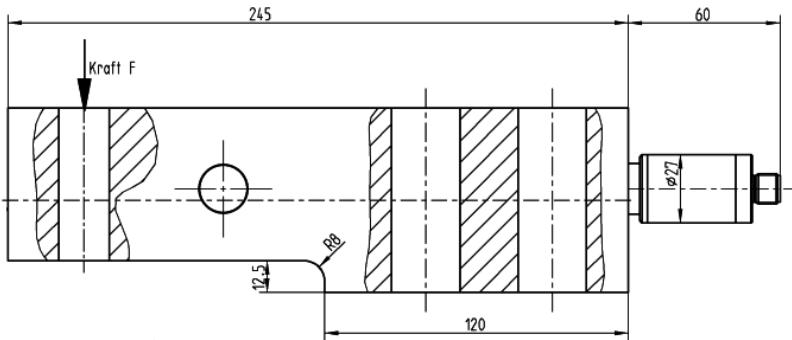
Maße und Krafteinleitung eines 30 kN bis 100 kN Scherstabes (Variante mit Durchgangsbohrung)
